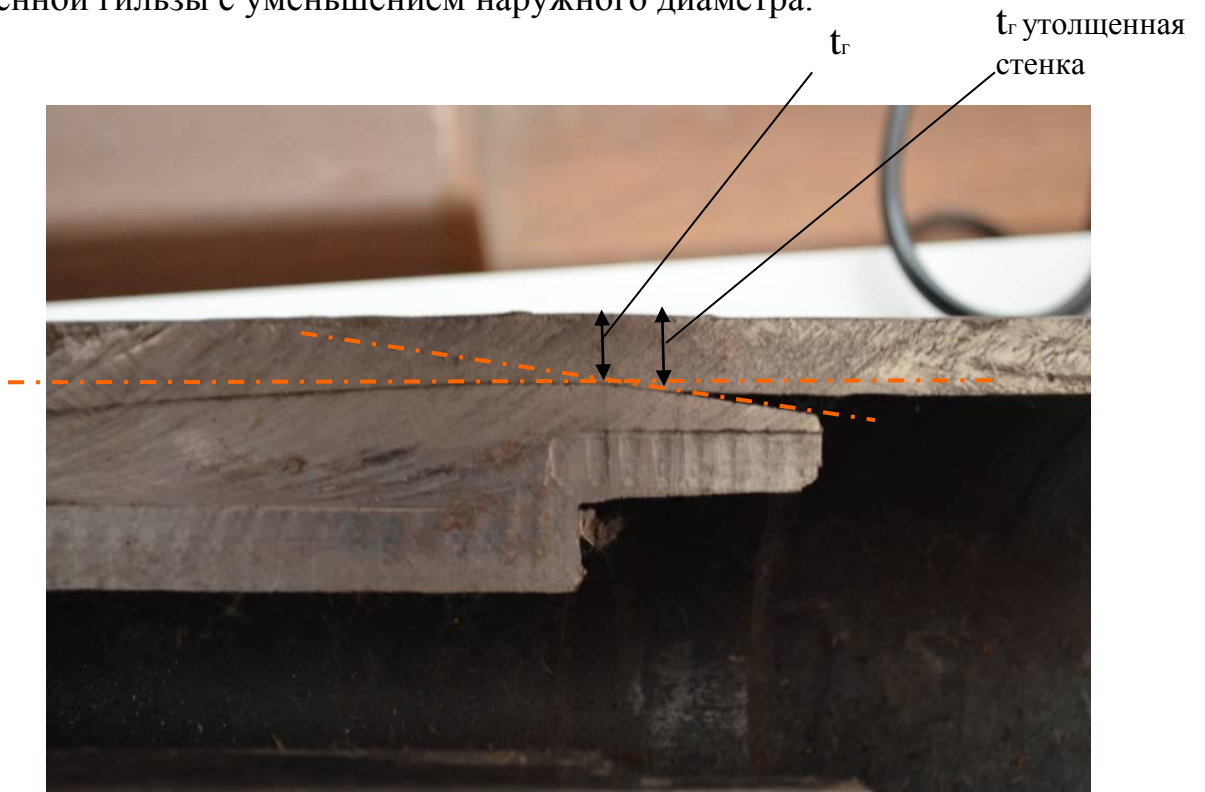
Фрагмент заторможенной заготовки в прошивном стане
